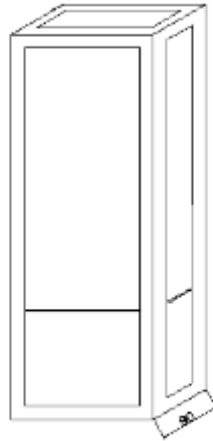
Maqueta de aluminio y acrílico. Parte externa de la maqueta.
